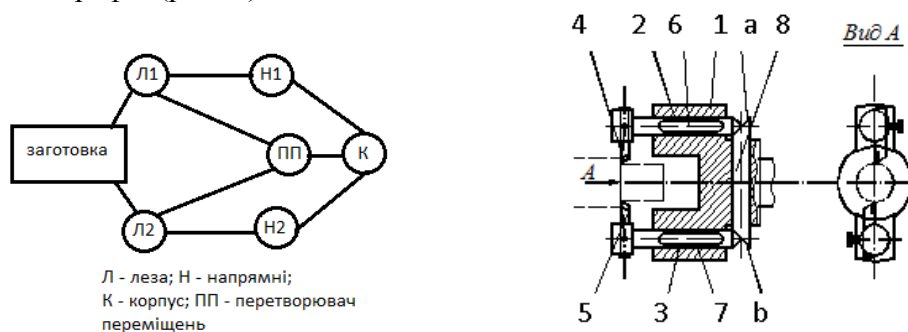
Графовий опис компоновки дворізцевої державки (1 – корпус; 2,3 – пальці; 4,5 – різці; 6,7 – шпоночні з'єднання; 8 – передавальний елемент)
